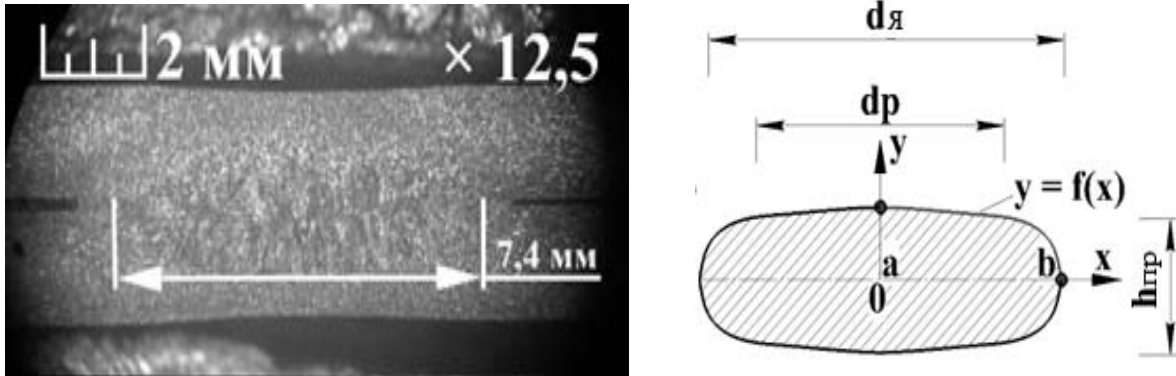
Макрошлиф и форма поперечного сечения литой зоны сварного соединения
